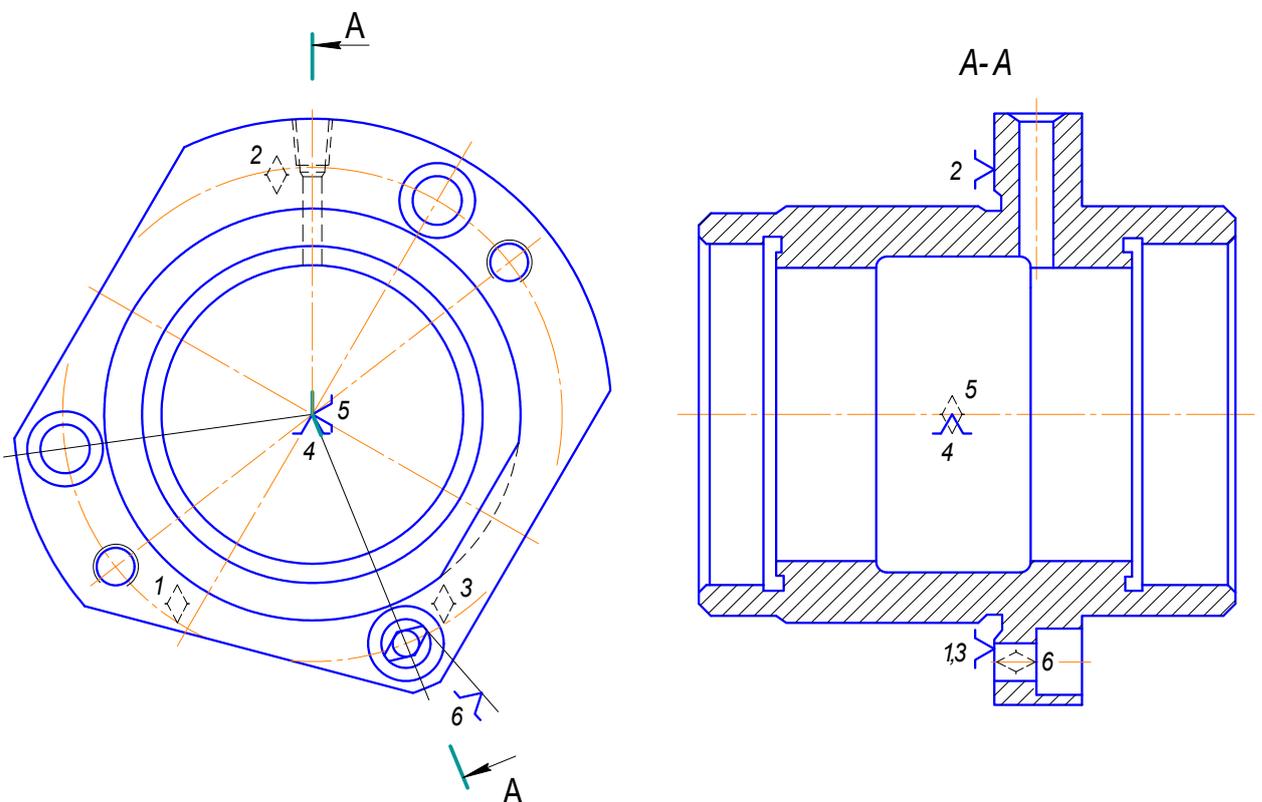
Схемо бозування деталі в пристрої для обробки отвору  $\varnothing 8,7$  мм
